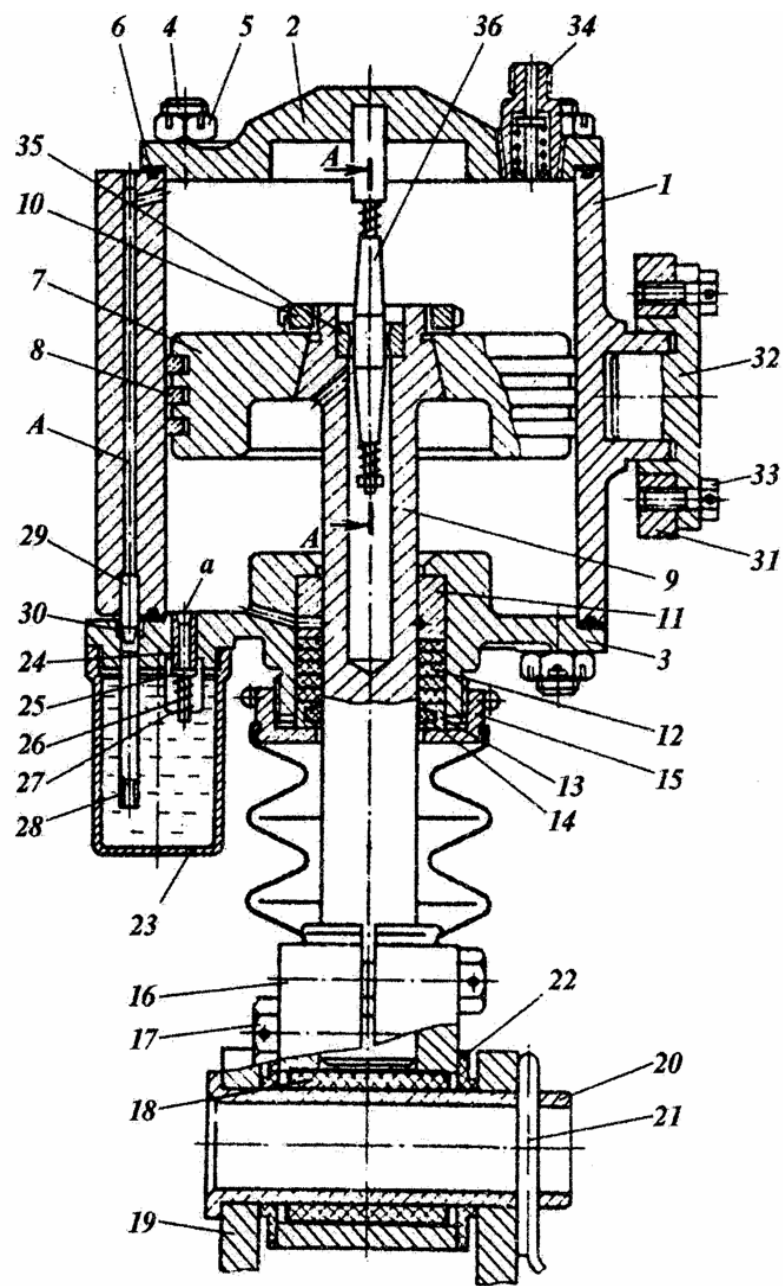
Пневматический гаситель колебаний с регулируемым дроссельным устройством
